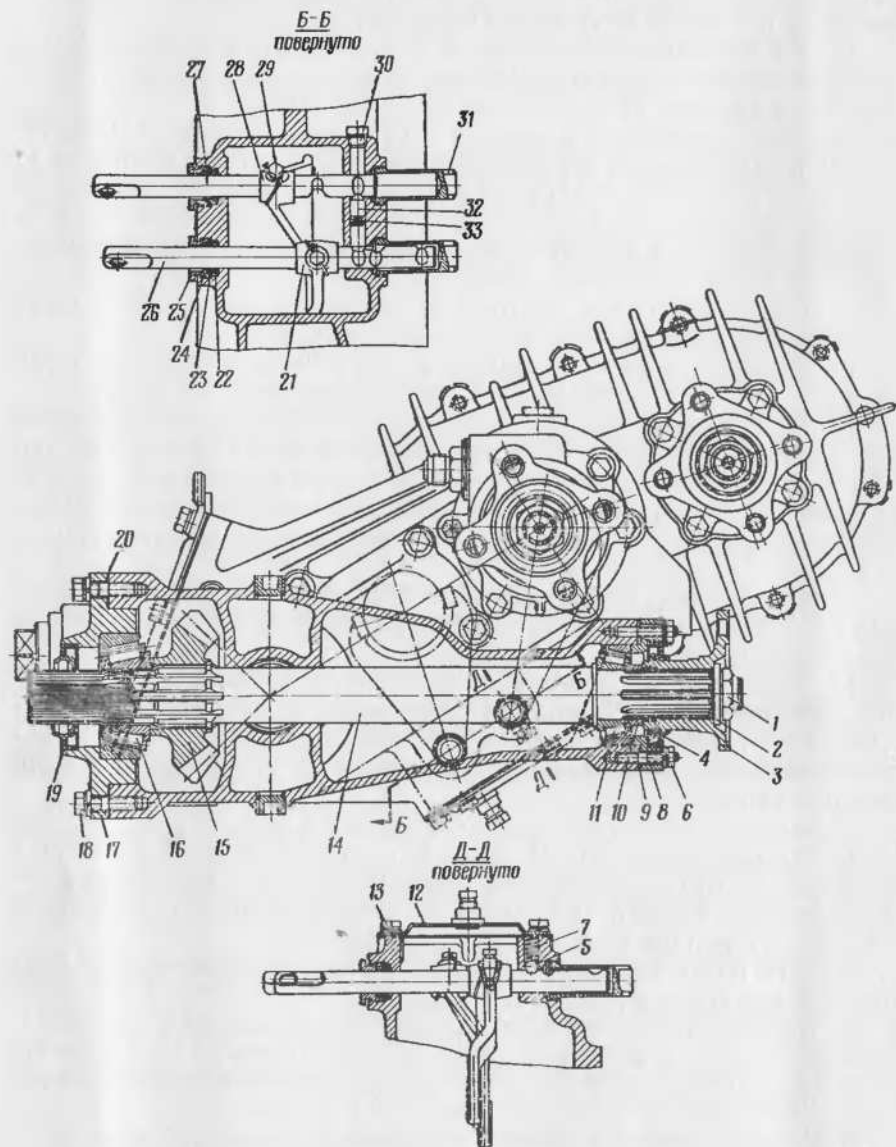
Коробка отбора мощности на дополнительные колеса:
